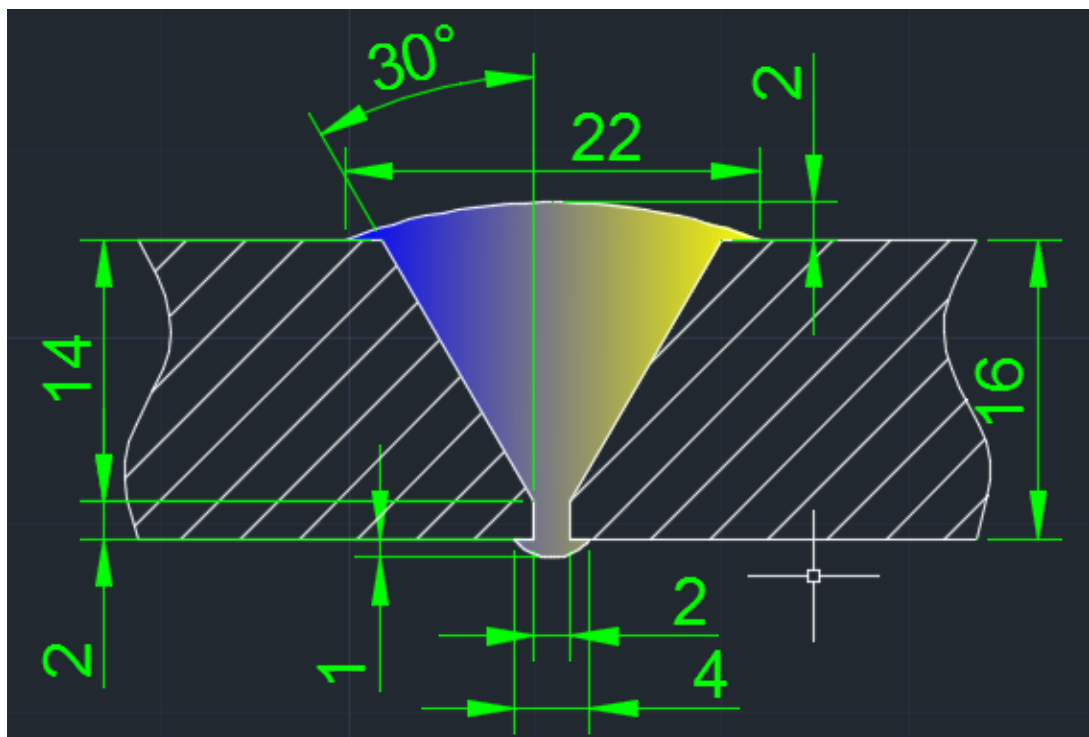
Сечение сварного стыка геометрической модели с обычной разделкой кромок
